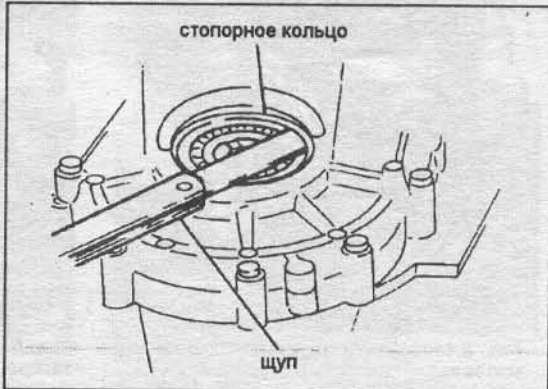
Контроль зазора между внешним кольцом подшипника и стопорным кольцом.
